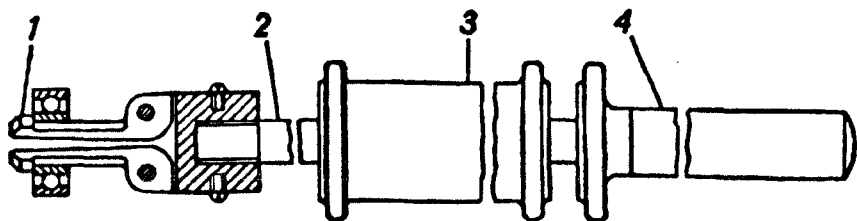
Съемник 7823-6090 для выпрессовки подшипника из коленчатого вала:
